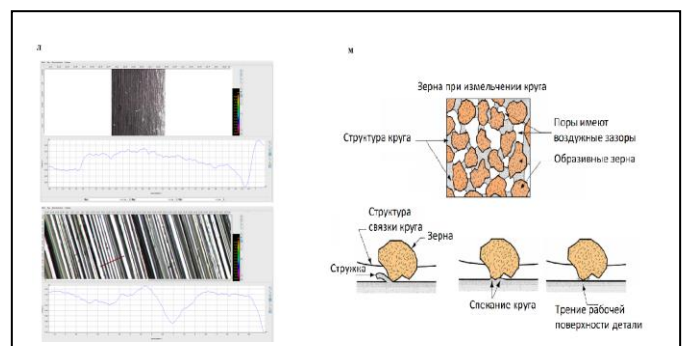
Сколы (к) при полировке зубчатых колес для выявления шероховатости поверхности зубчатой части (м)
